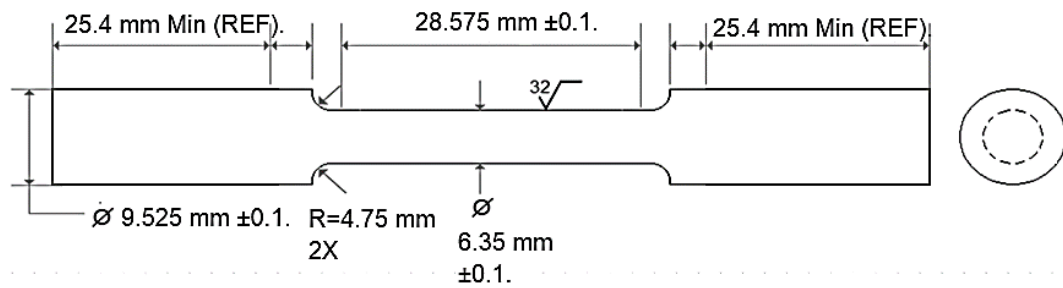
Dimensiones de la probeta sub-size de acuerdo con ASTM E8 [38].
